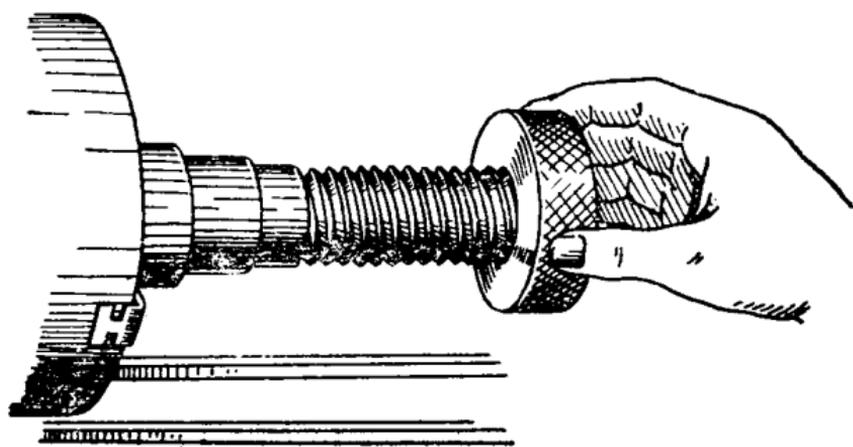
Проверка наружной резьбы предельным резьбовым кольцом.
